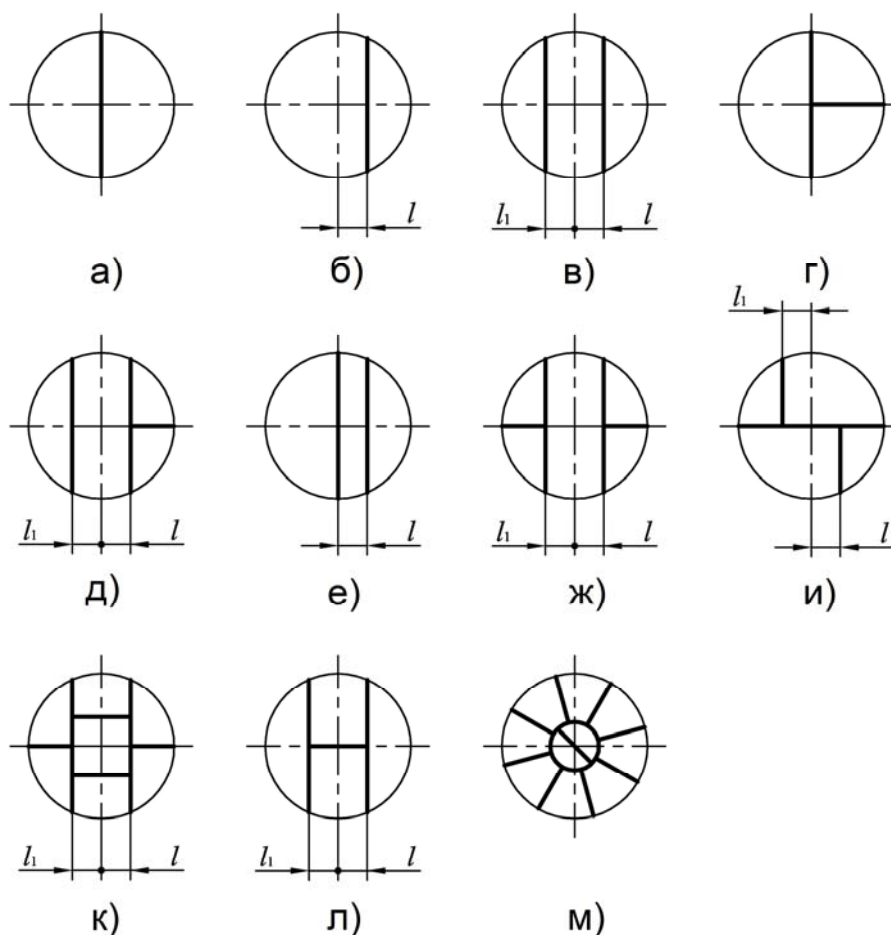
Расположение сварных швов заготовок выпуклых днищ
